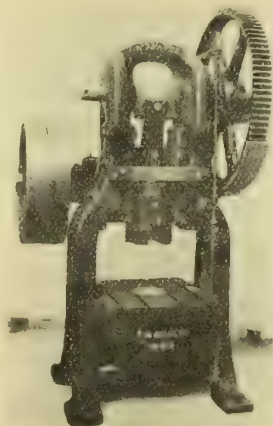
Presse à emboutir l'aluminium. Presse pour objets de grand diamètre.
